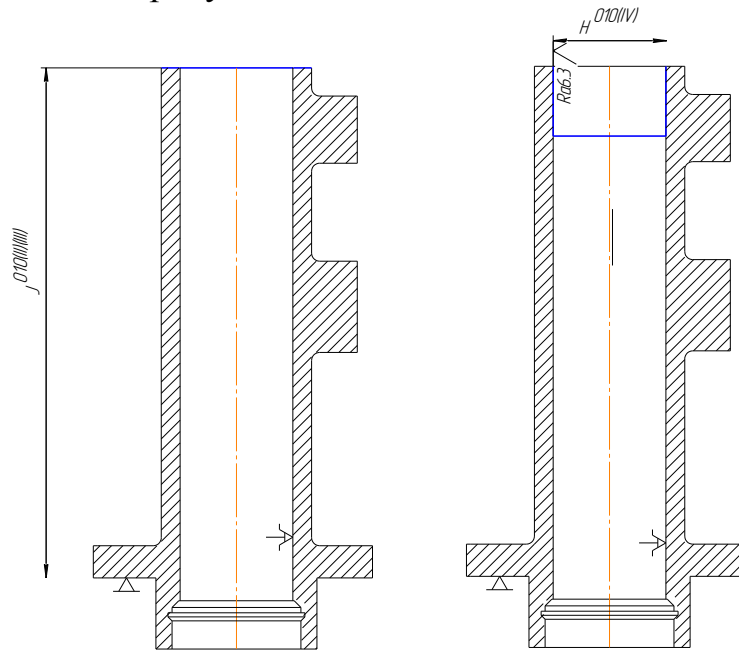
Полуцистовое и чистовое фрезерование торца, развертывание отверстия
